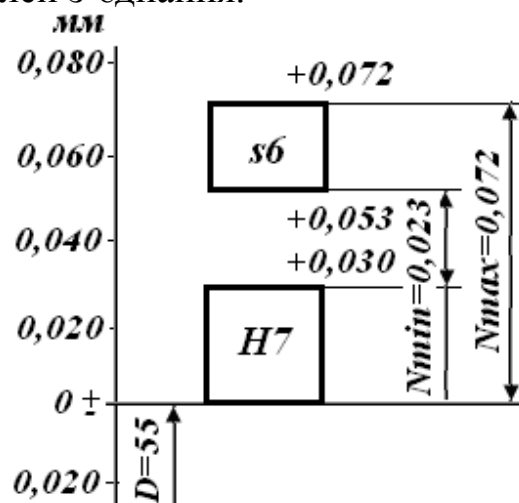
Схема розташування полів допусків деталей з'єднання $\varnothing 55H7/s6$
